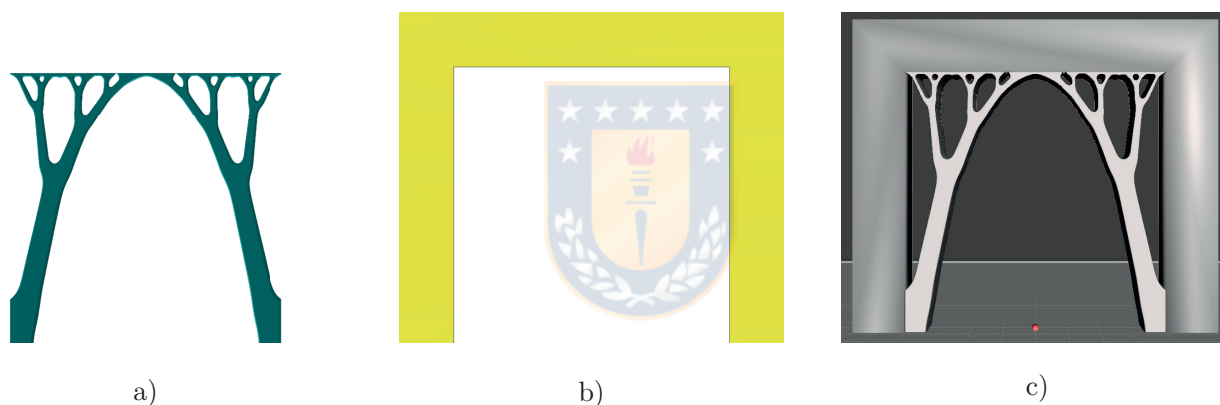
Ensamblaje soporte-pieza. En (a) soportes optimizados en Matlab convertidos a formato STL. En (b) pieza diseñada en Inventor que se busca imprimir. En (c) ensamblaje de los soportes con la pieza utilizando el software Meshmixer.
